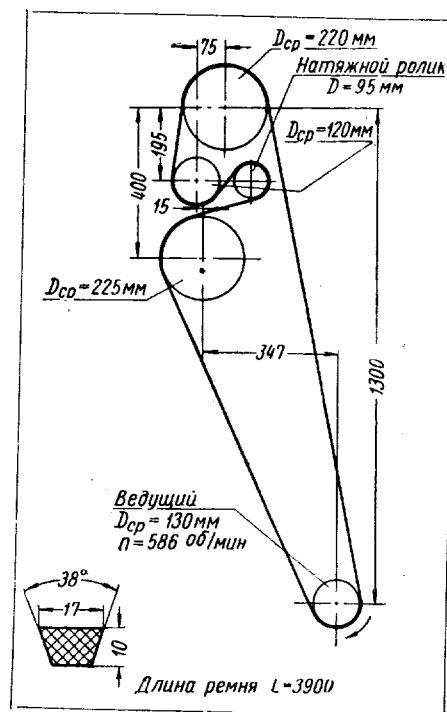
Схема клиноременной передачи зерноуборочного комбайна с одинаковым направлением вращения ведущего и ведомых валов
